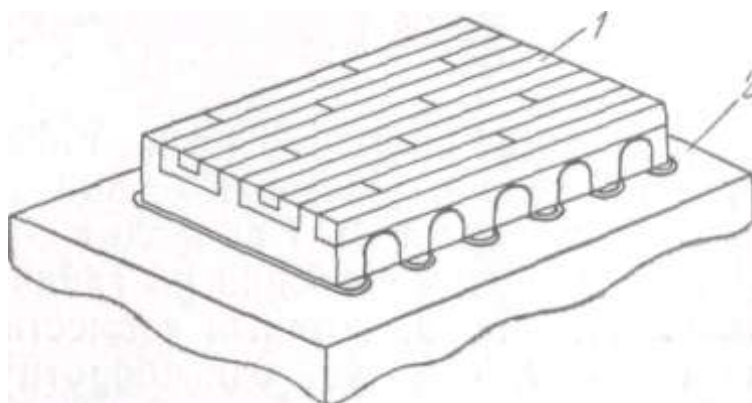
Наладка к магнитным плитам, изменяющая расположение полюсов, их размеры и межполюсные расстояния: 1- переходник; 2 - магнитная плита.
